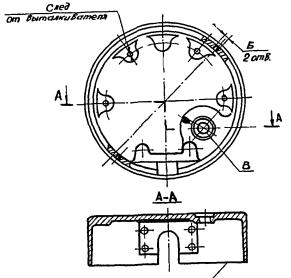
Корпус (3.9210.174) Поз.3. Рис.4
